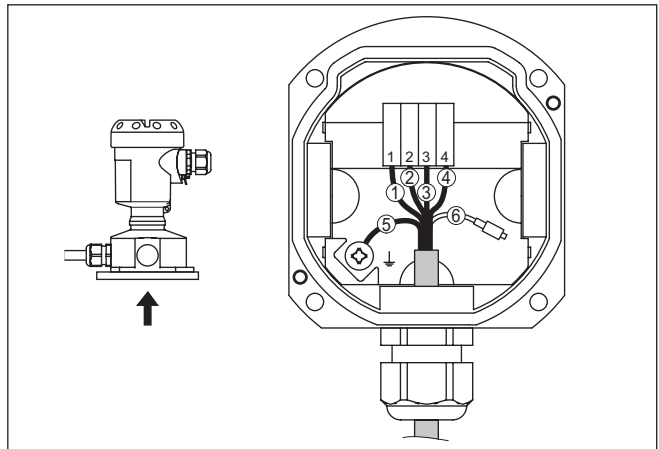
Anschluss der Prozessbaugruppe im Gehäusesockel
